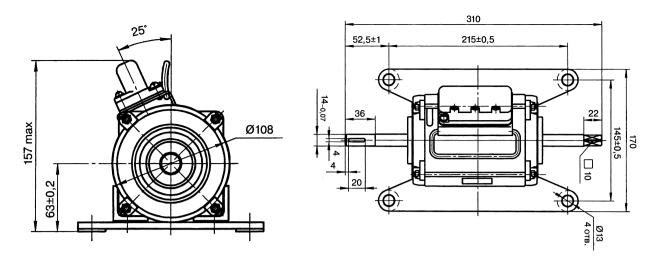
Габаритные и присоединительные размеры электродвигателей типа MCA.M-0,15BCП; MCA.M-0,25BCП; MCA.M-0,3BCП.
